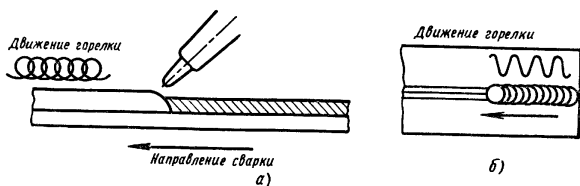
Движение горелки при сварке по отбортовке: а — спиралеобразное; б — колебательное
